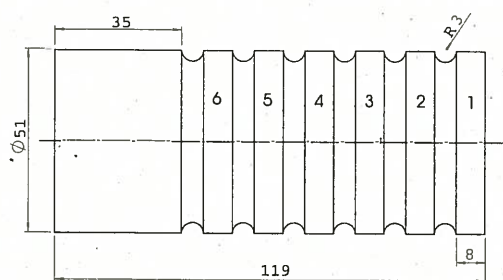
Provete de ensaio – 6 superfícies de corte
